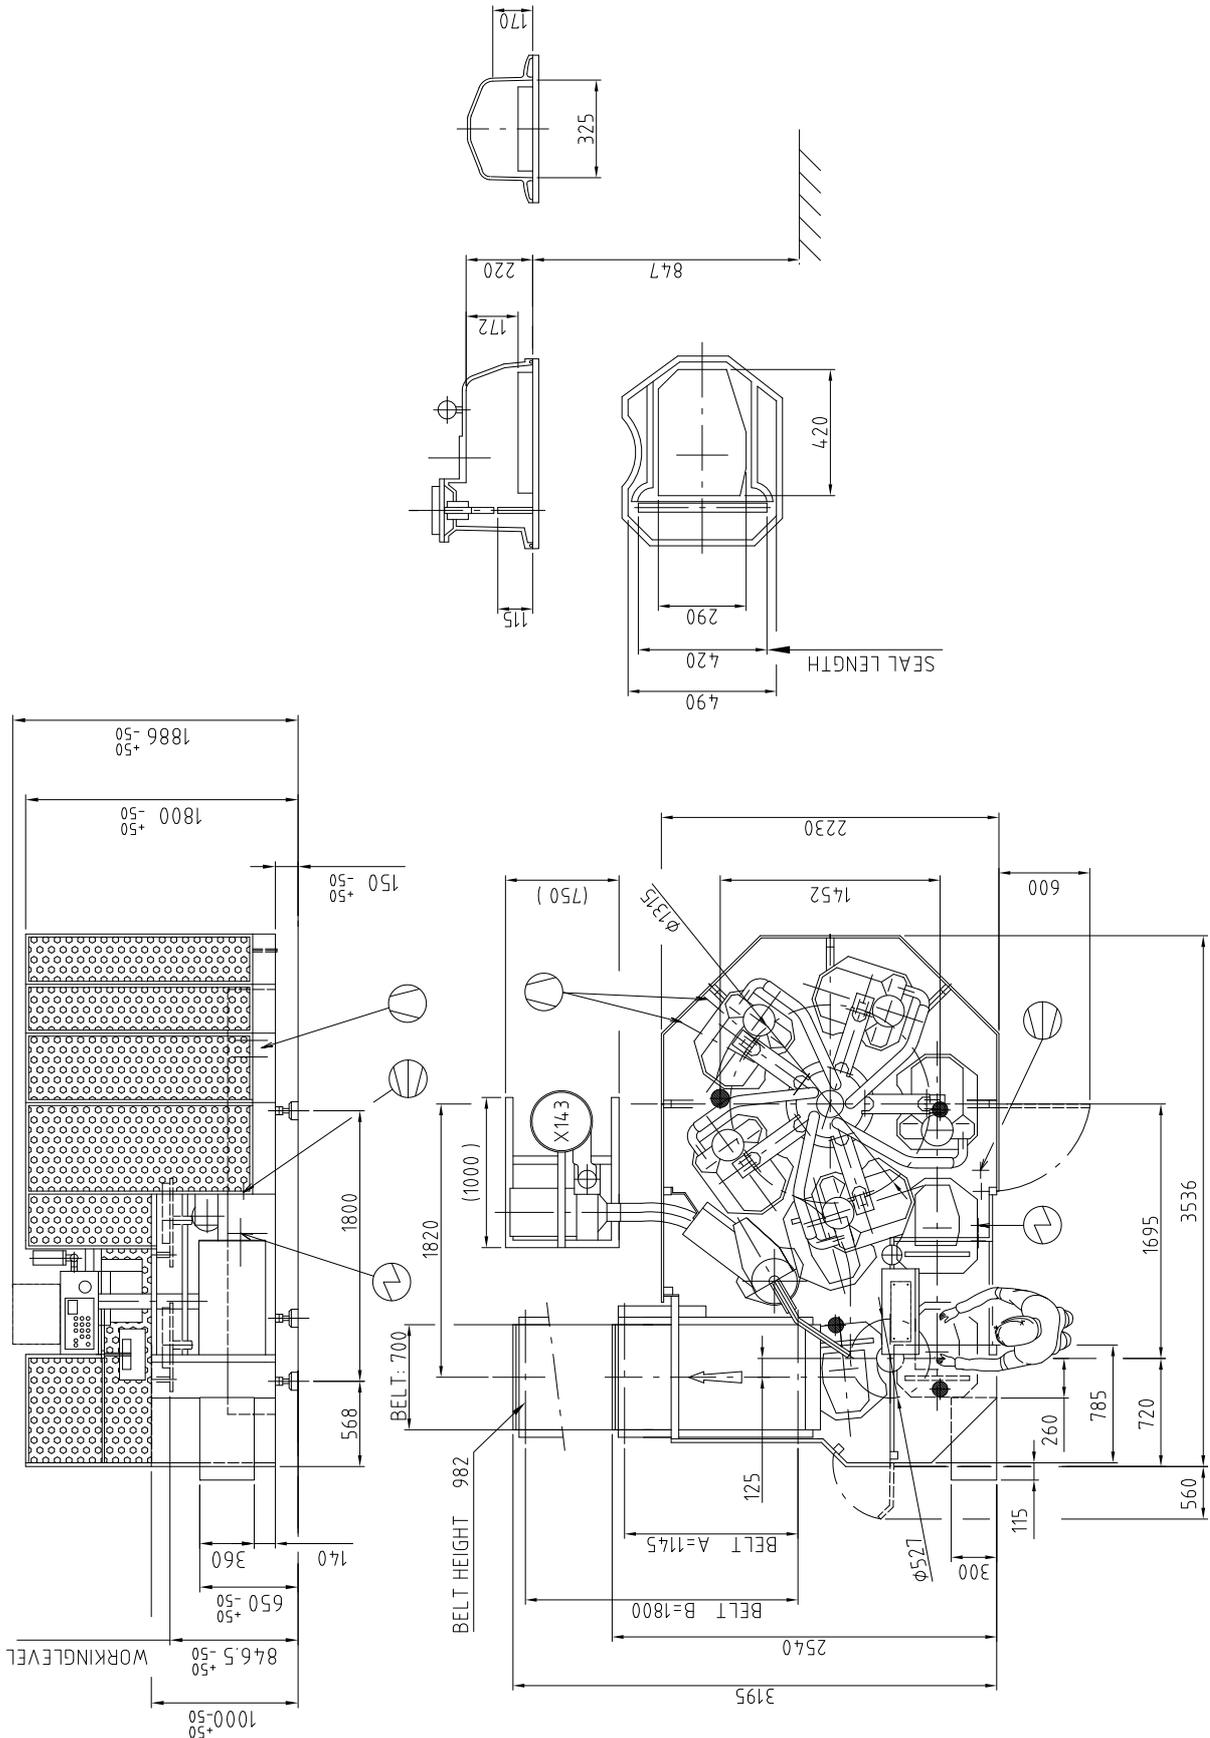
, Dimensiones LR (flujo del producto de izquierda a derecha)
